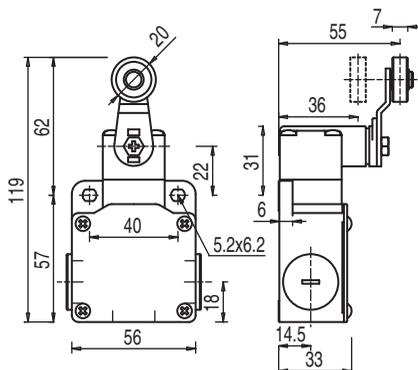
Dimensions des S300-M0C3-M20-31 et S300-M13C3-M20-31 en mm
